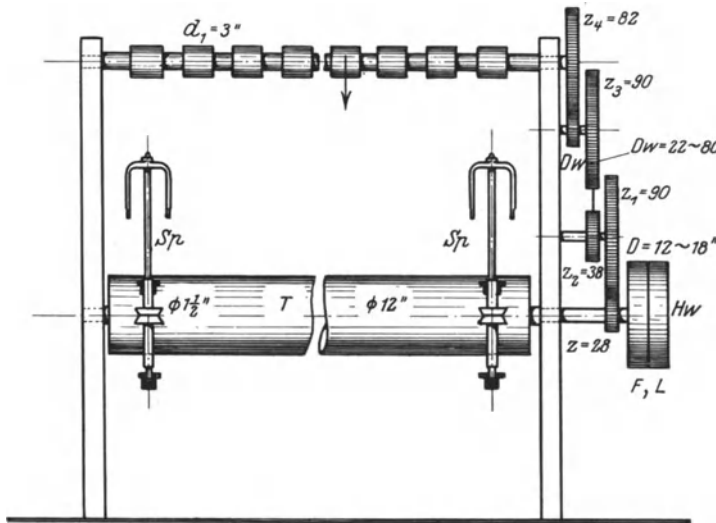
Getriebezeichnungen zur Zwirnmaschine.
